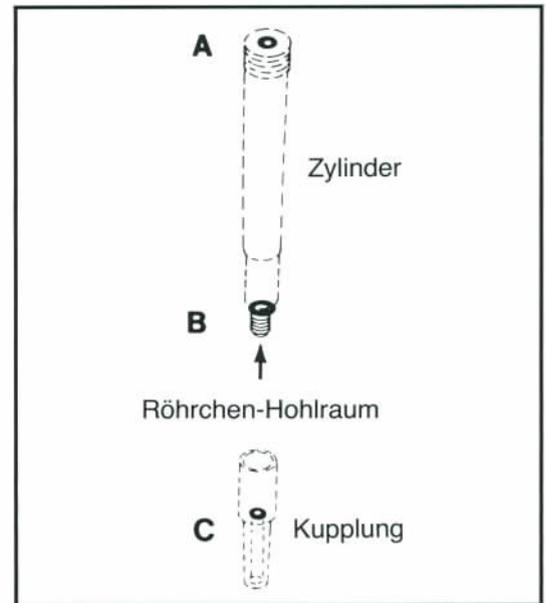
Zylinder und Kupplung auseinandergeschraubt mit O-Ringen
